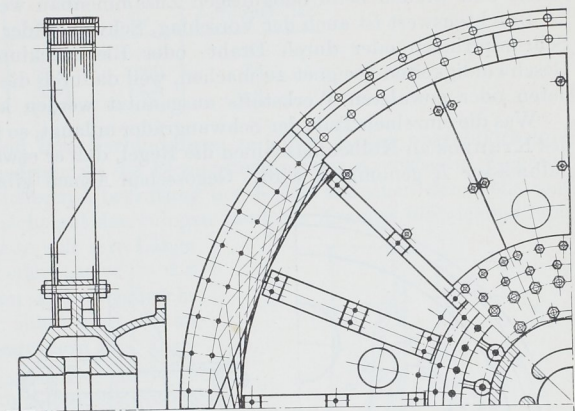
Schwungrad einer Walzenzugmaschine aus Blechplatten.
